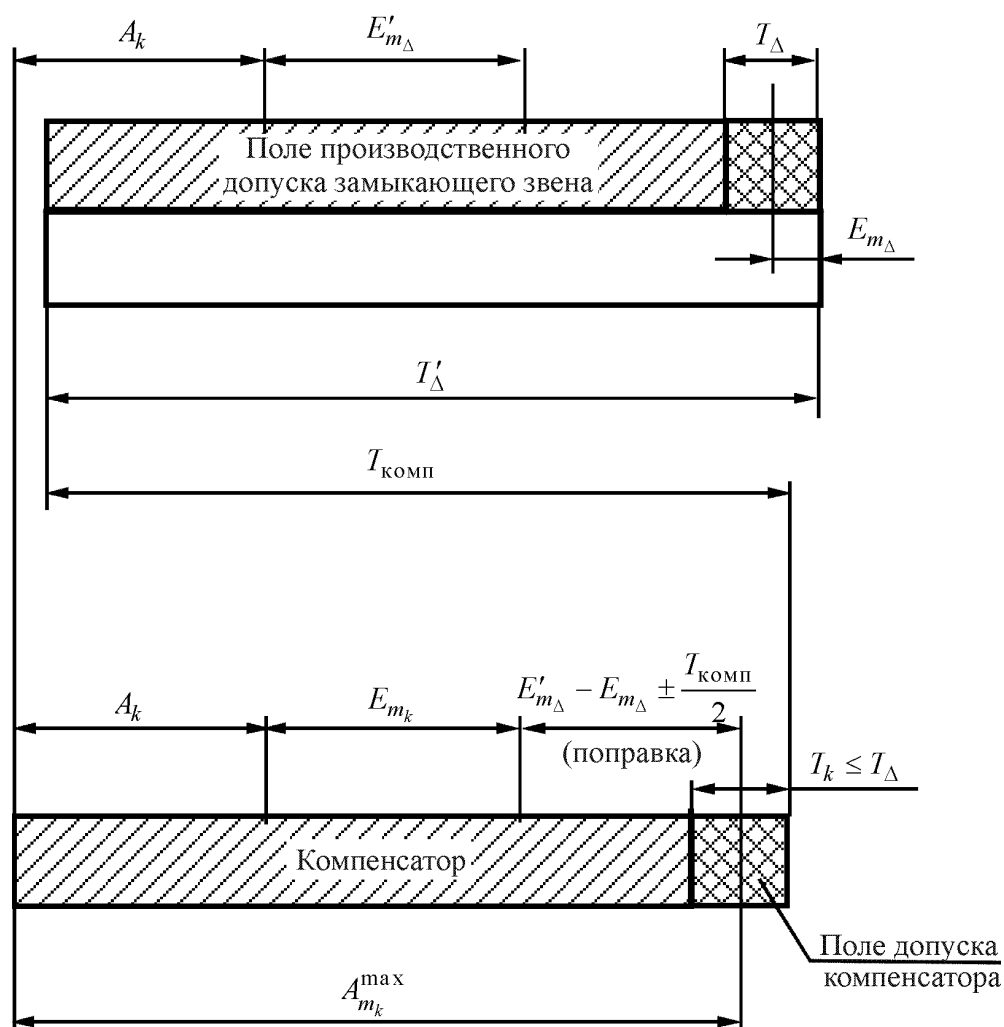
Схема расположения полей допусков компенсатора и замыкающего звена сборочной размерной цепи
